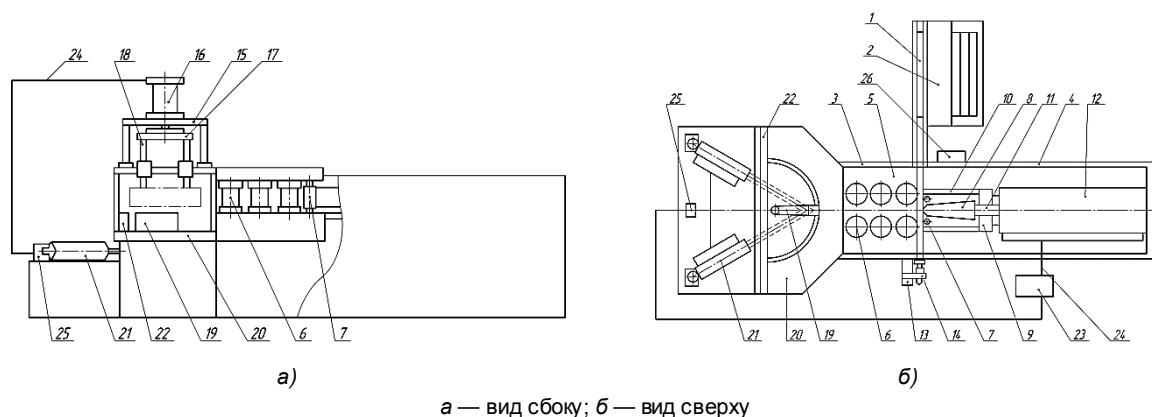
Принципиальная схема модернизированного прокатного стана для парной прокатки заготовок направляющих элементов пневмоподвески
